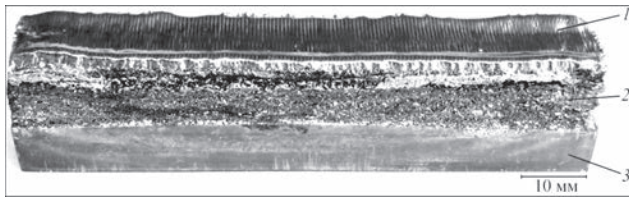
Образец изделия, изготовленный методом электронно-лучевой 3D-наплавки: 1 — верхний слой наплавленного металла; 2 — промежуточный слой металла с частицами нерасплавленного порошка; 3 — подложка из титана
